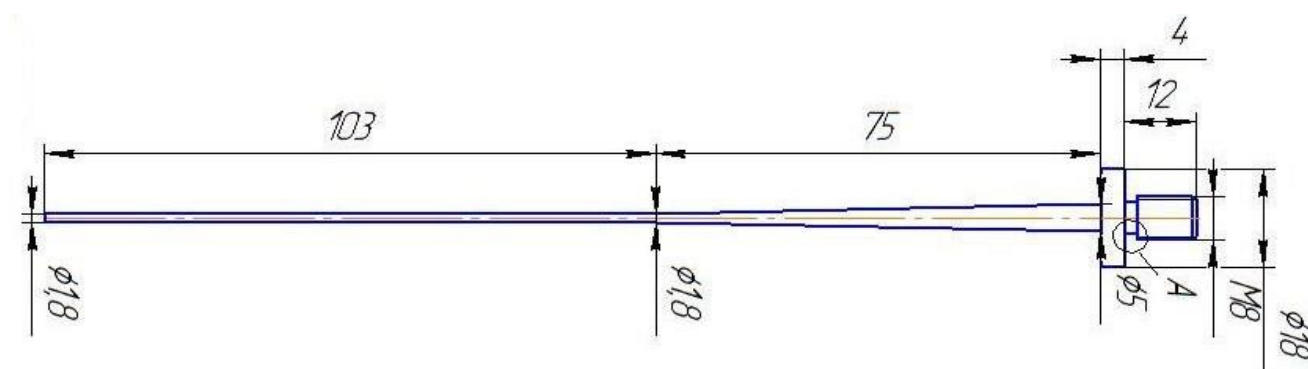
Ультразвуковой излучатель для чрездренажного акустического
